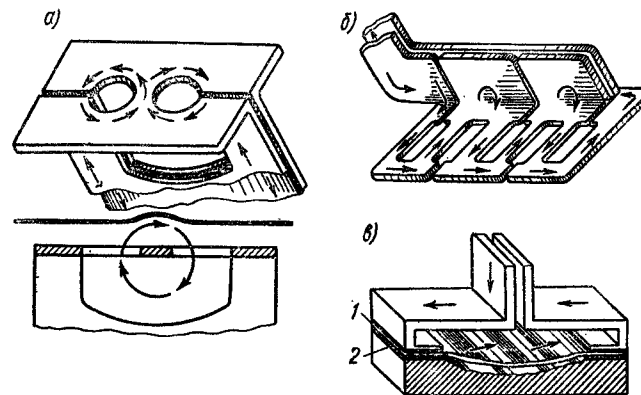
Типы индукторов: а — двухвитковый; б — для гофрирования; в — с пропусканием импульсного тока через плоскую заготовку; 1 — заготовка; 2 — изоляция
